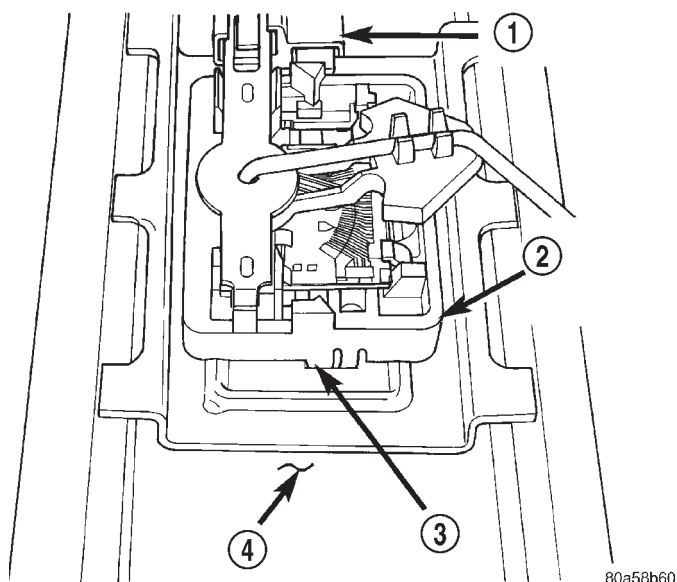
Lengüeta de desenganche del conjunto transmisor de nivel de combustible
